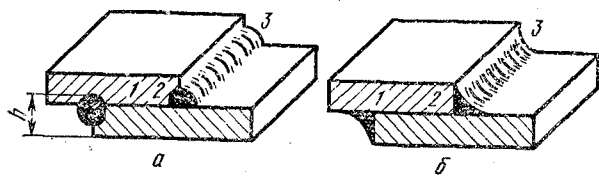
Форма и элементы сварного (а) и паяного (б) швов при соединении внахлестку
